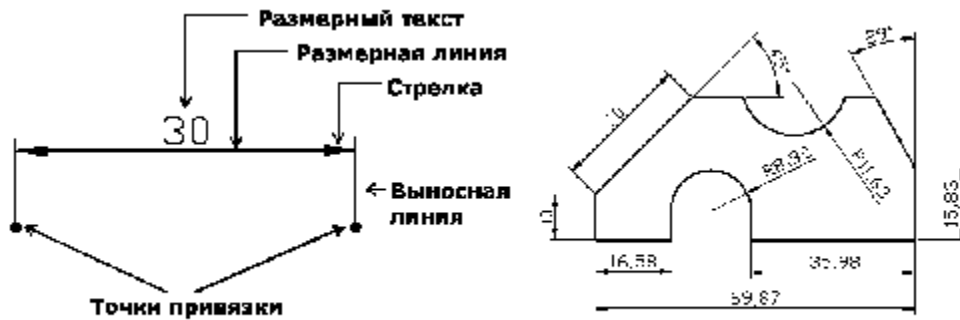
Элементы размерного блока и пример образмеренного чертежа
